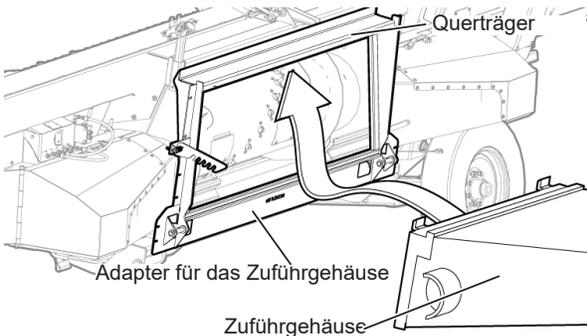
Zuführgehäuse in die Adapterplatte einsetzen
